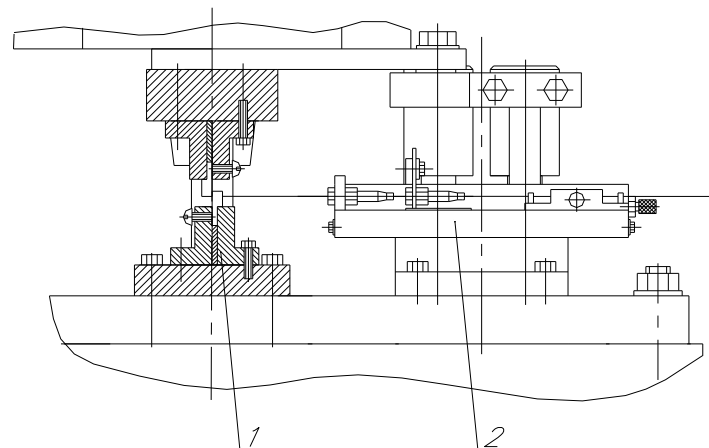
Схема установки для исследования износа режущих кромок ножей штампов (1 – штамп для резки проволоки; 2 – клиновья подача)
